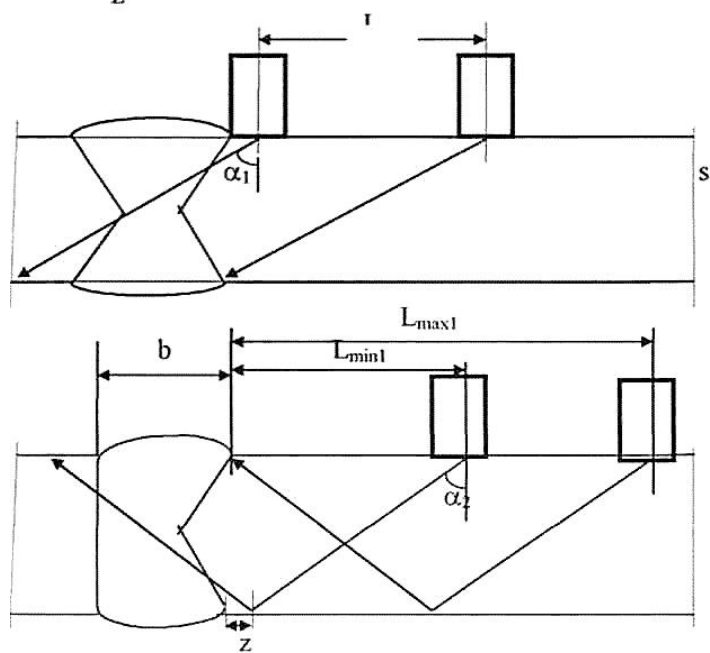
Схема сканирования стыкового сварного шва:
